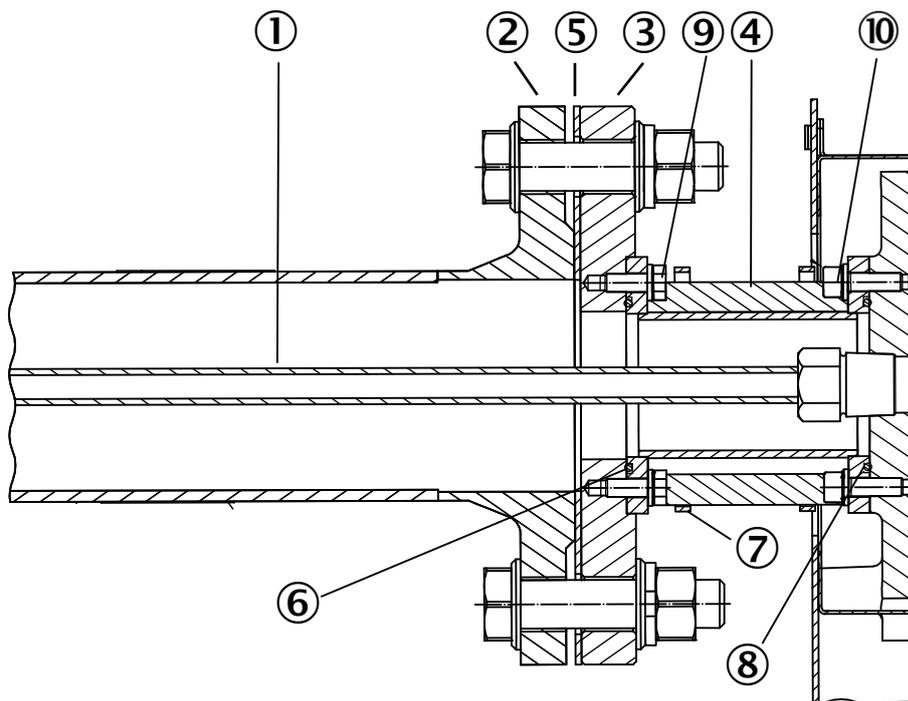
Vue de détail du tube de prélèvement de gaz non chauffé
